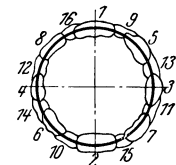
Reihenfolge beim Schweißen auf einer Welle.
